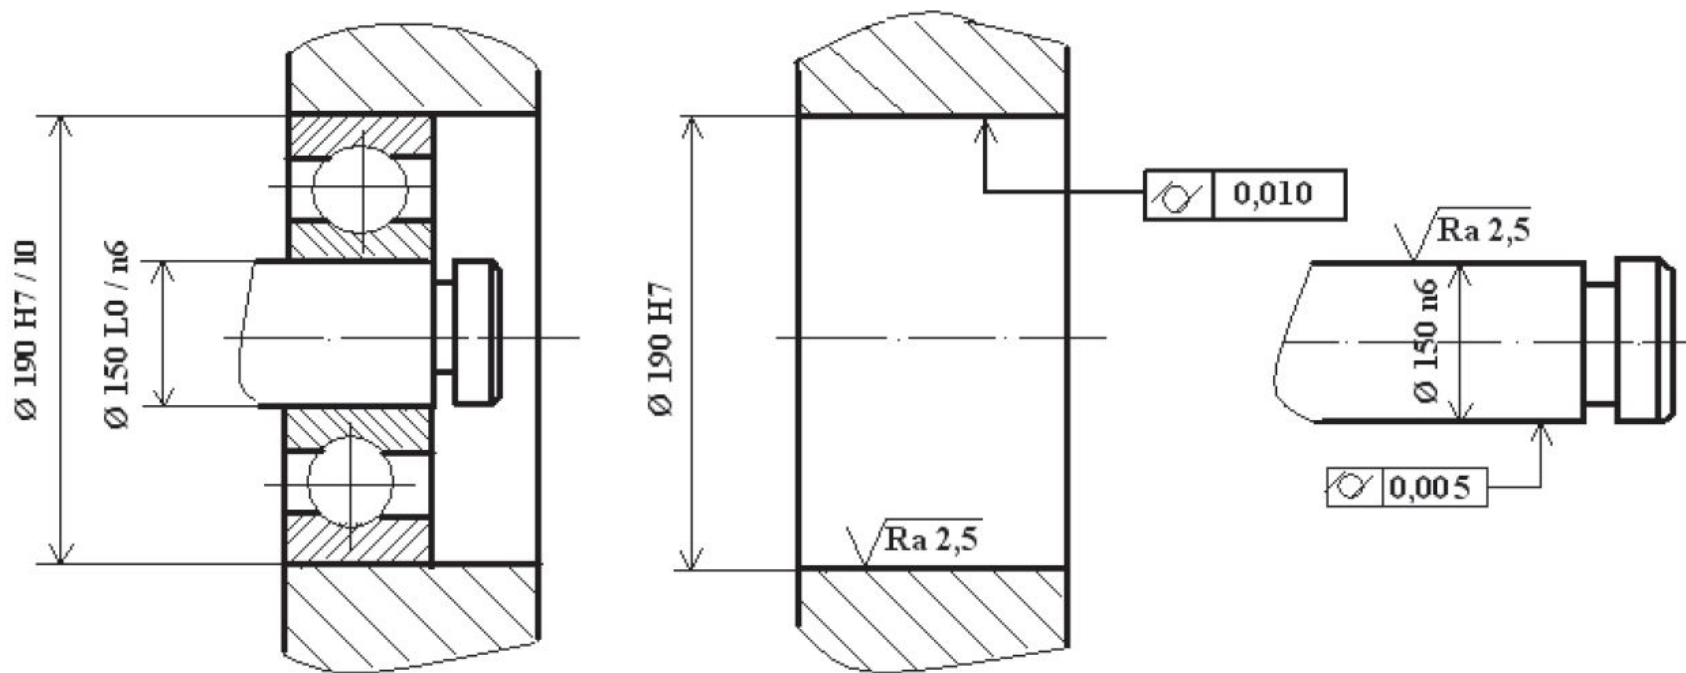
Эскиз подшипникового узла и детали подшипникового соединения
